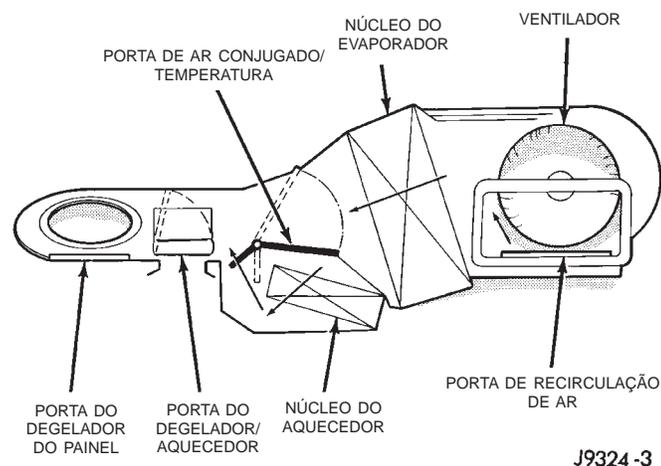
Sistema Comum de Aquecedor-Ar Condicionado com Ar Conjugado
